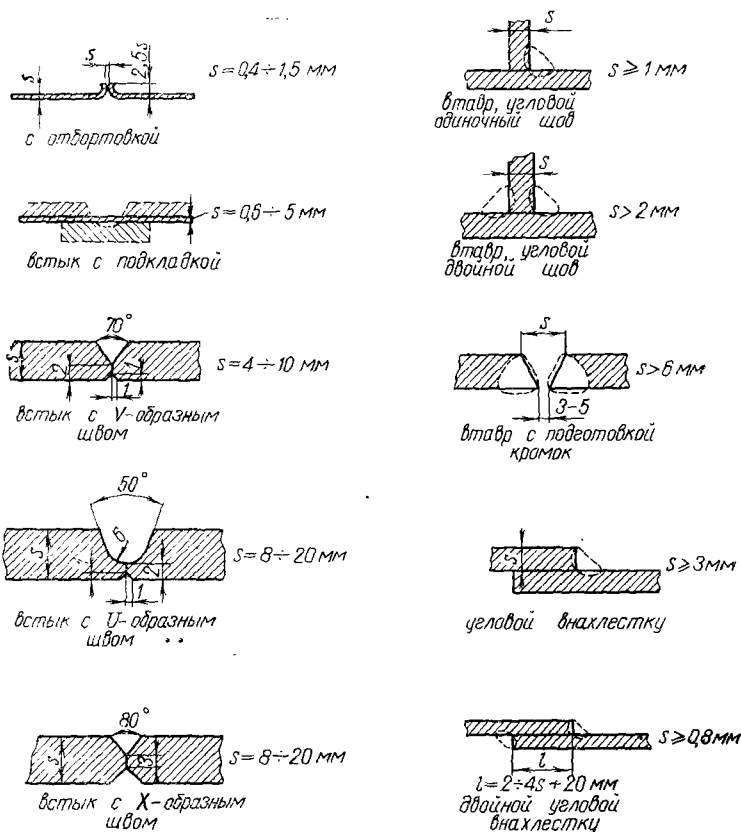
Сварные соединения из алюминиевых сплавов
